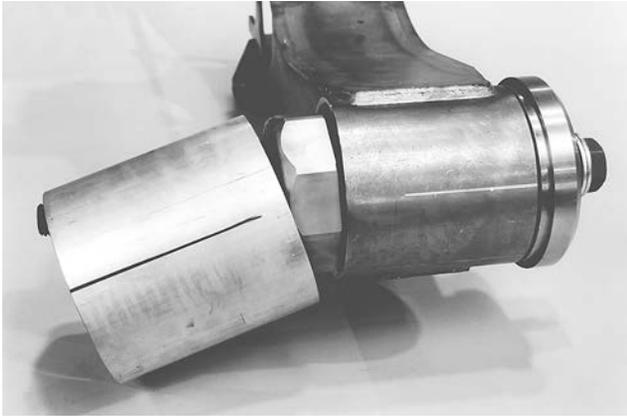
Continúe apretando el tornillo hexagonal después de que el tubo de transición se caiga
